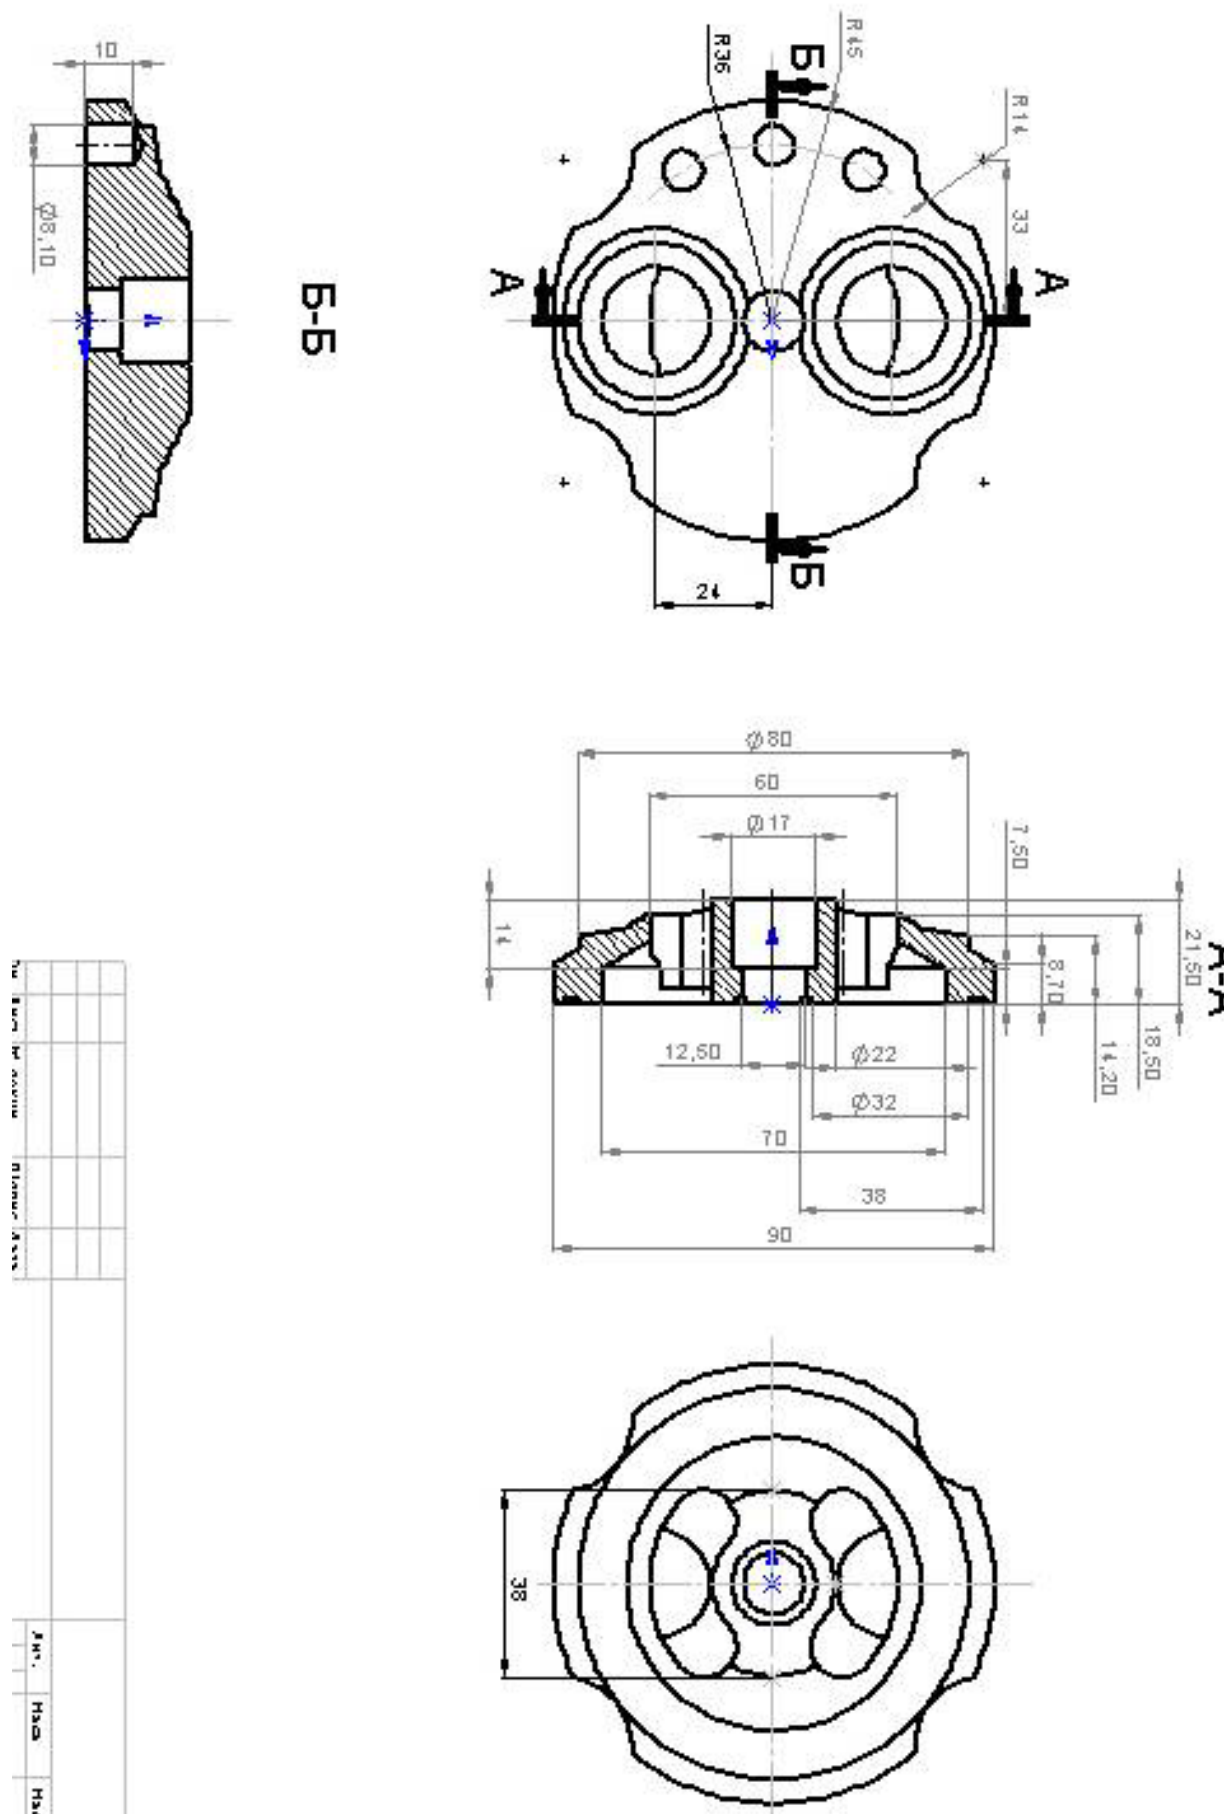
Креслення виконане в Solidworks. Спрощений варіант
